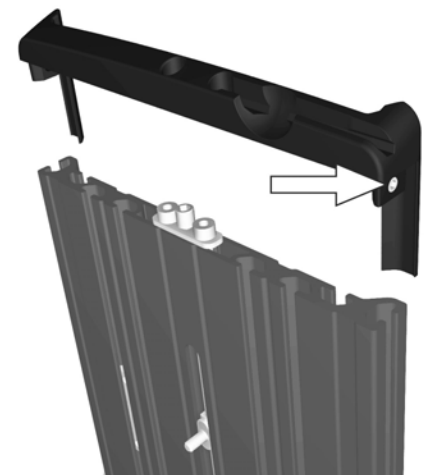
Die Endabdeckung des Rückenlehnenprofils ist mit einer Schraube auf der linken und einer Schraube auf der rechten Seite gesichert.
